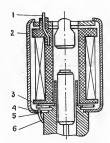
Электромагнитный клапан: 1 — клемма; 2 — кожух; 3 контактная пластина; 4 — паз; 5 — клей; 6 — провод.
